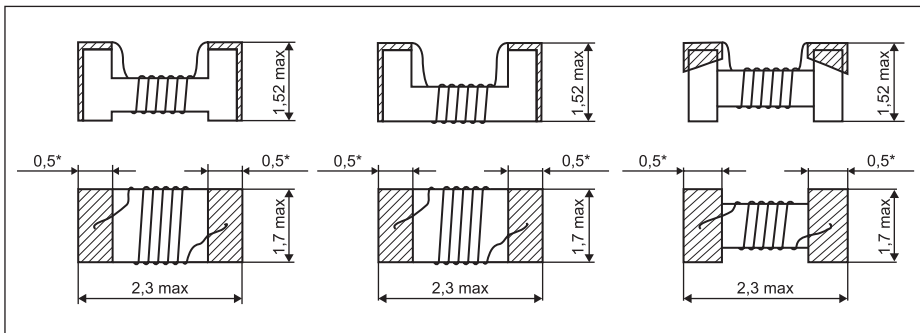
Общий вид, габаритные и установочные размеры микроиндуктивностей KIB21K
